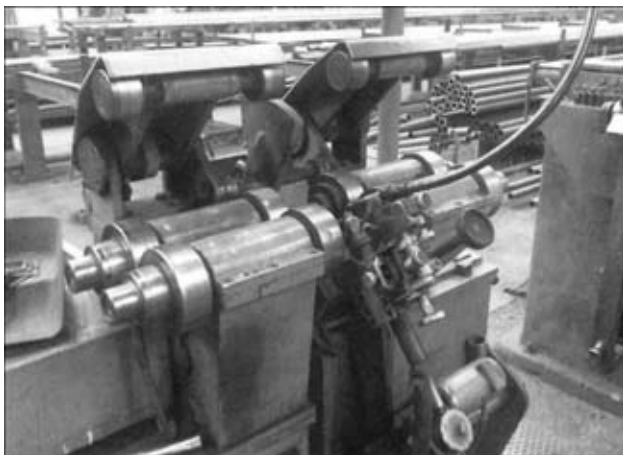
Трубосварочная установка типа VKW со сварочной головкой, установленной под стыком труб (с верхней подачей присадочной проволоки)
